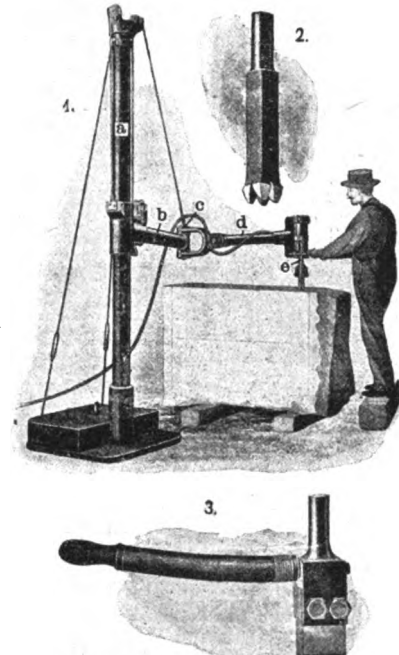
Mit Pressluft betriebene Steinbearbeitungsmaschine.
